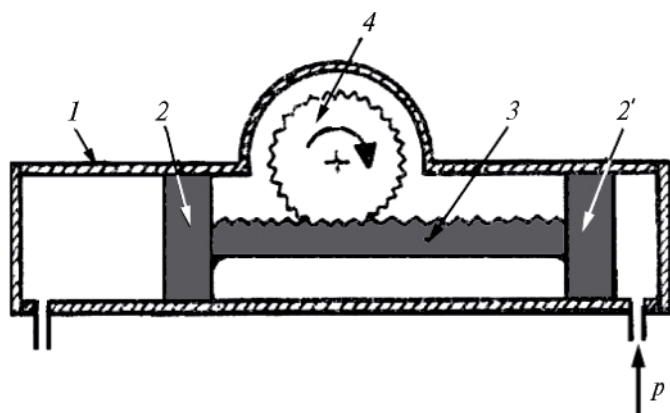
Поворотный пневмодвигатель с зубчато-реечной передачей
